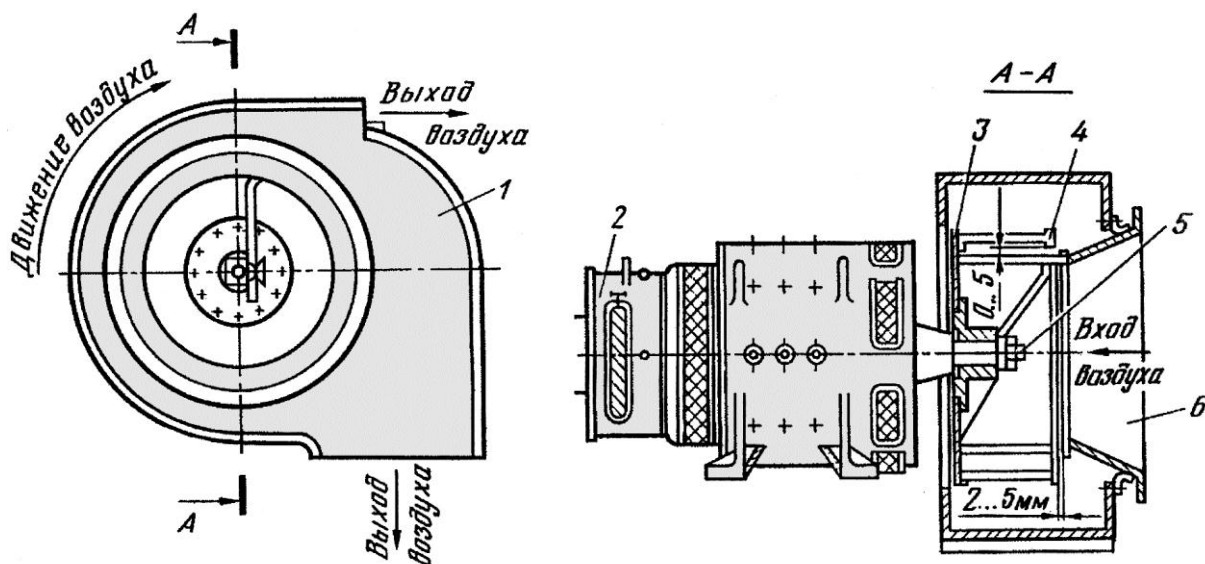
Центробежный вентилятор Ц13-50 № 8 с двумя выходными патрубками
